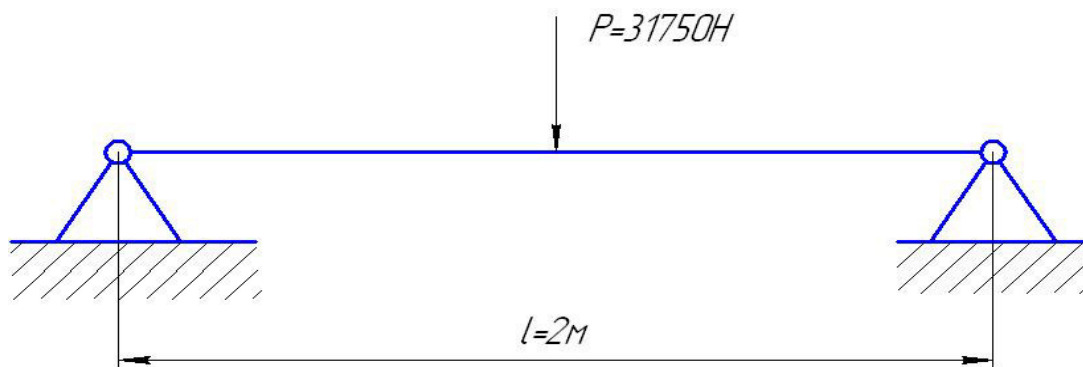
Схема к расчету лонжерона верхней рамы
